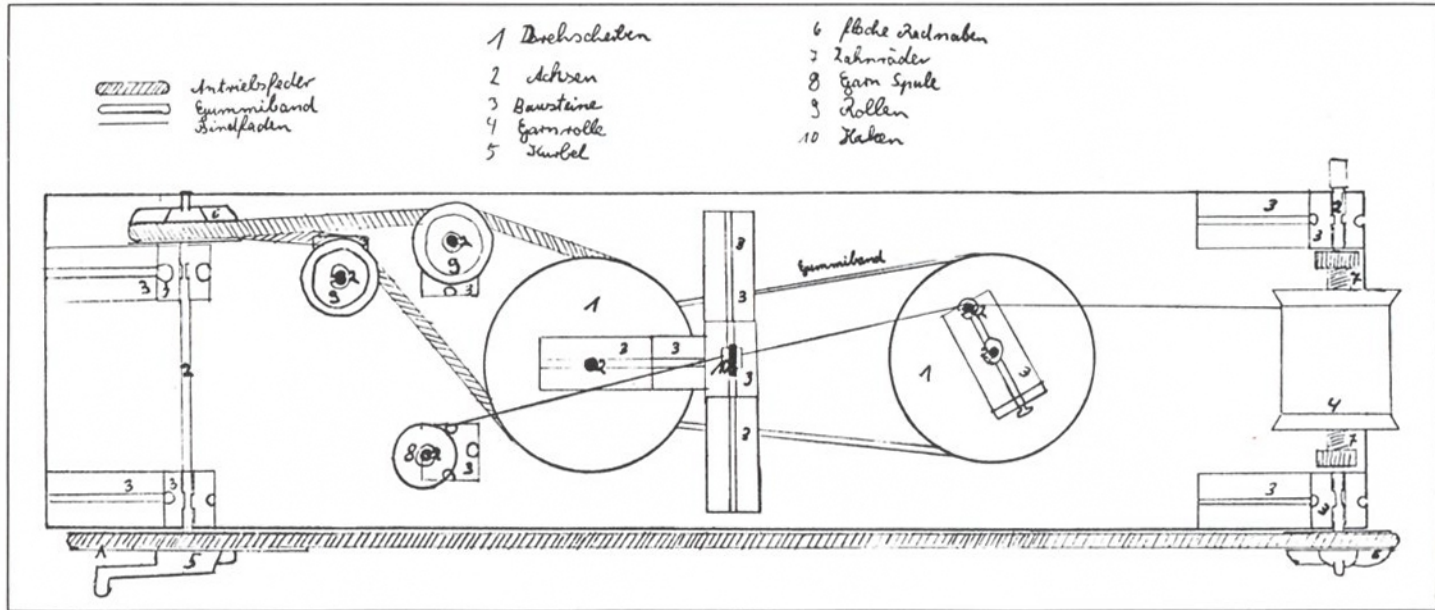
Zeichnung der um 180° gedrehten Aufwickelmaschine 6.5
